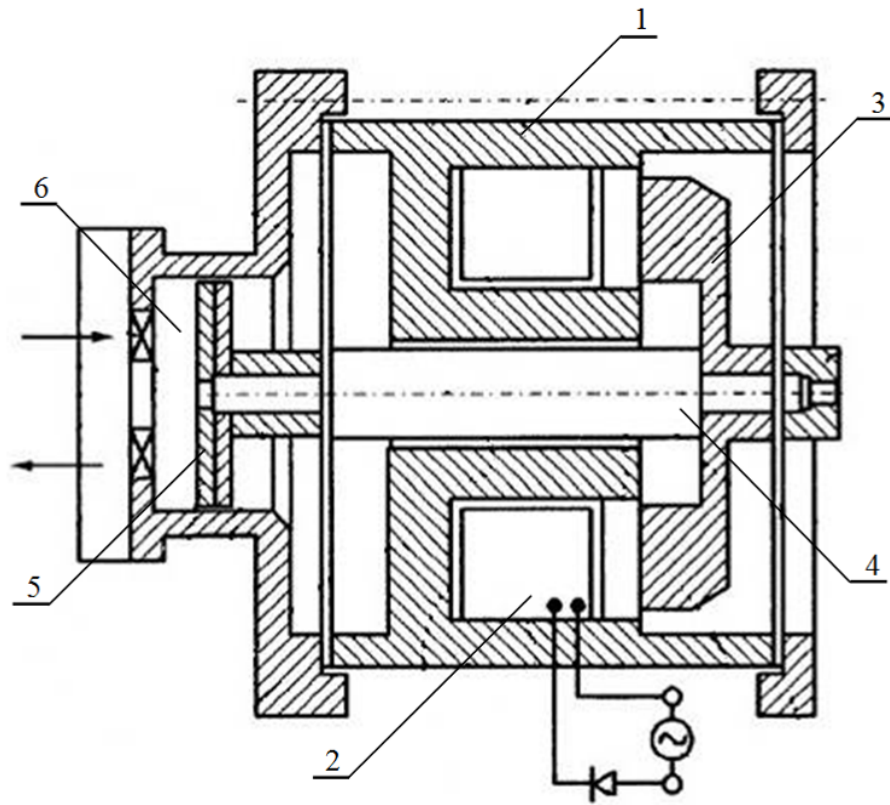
Электромагнитный компрессор для небулайзера
